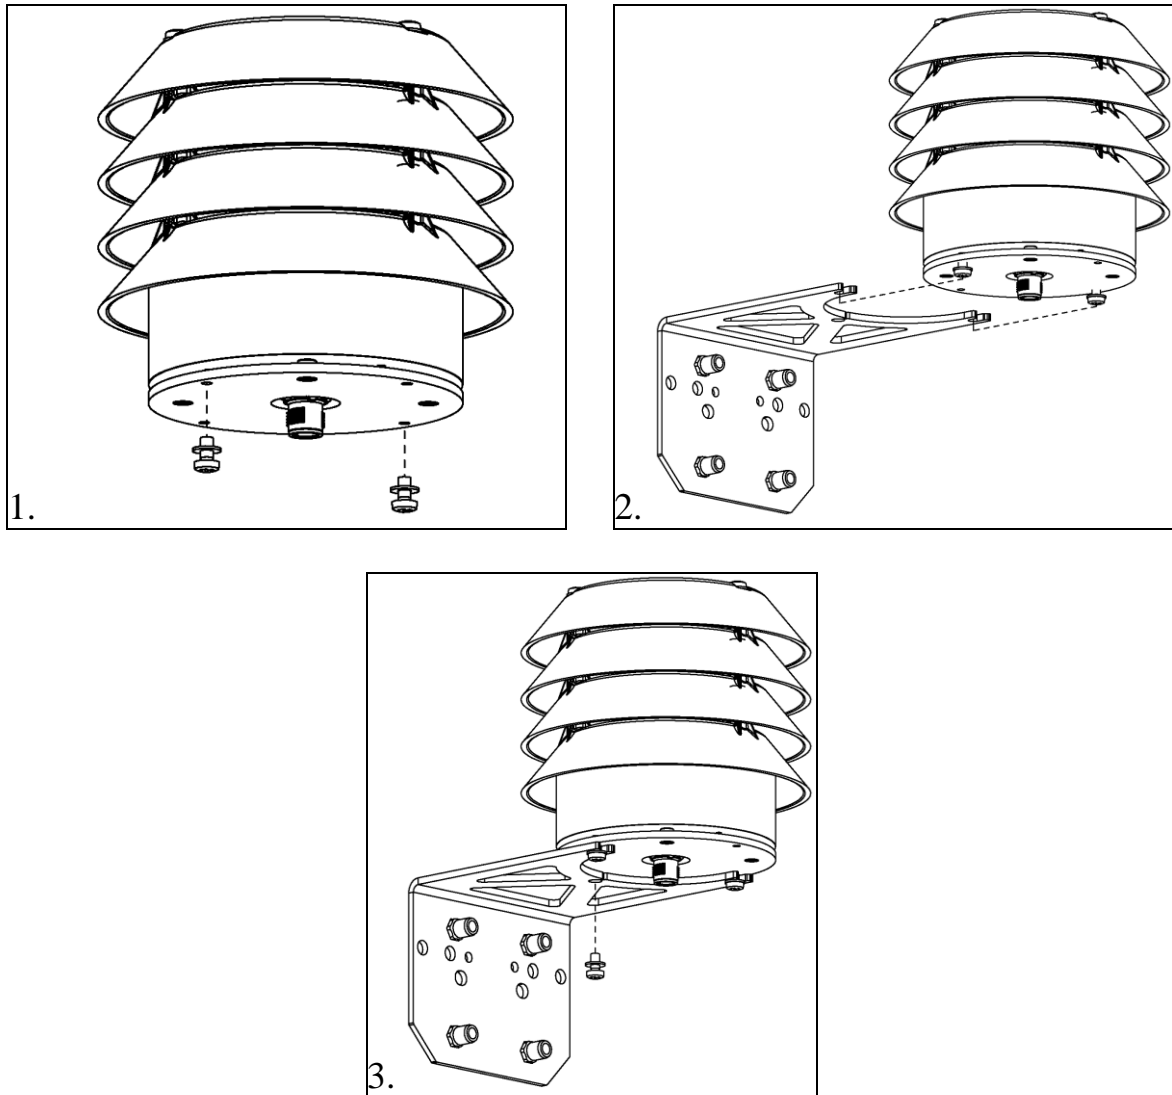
Схема установки приладу AQT420 на монтажний кронштейн
